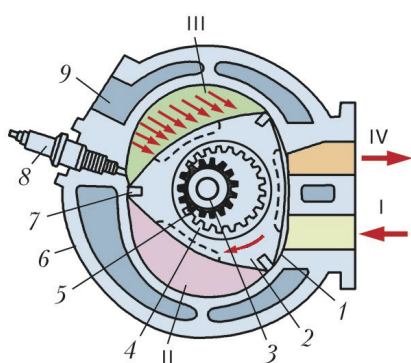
Разрез двигателя Ванкеля и его основные детали:
